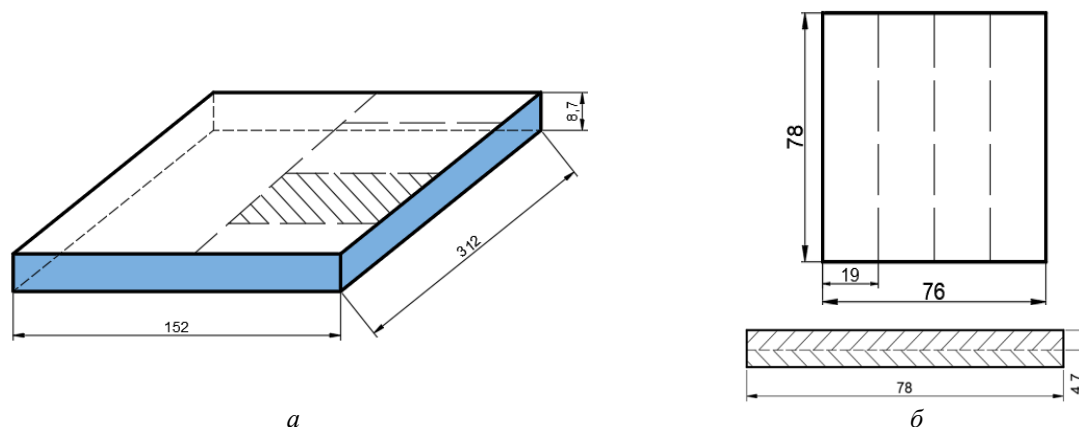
Схема вырезки образца из сваренного КМ (а) и подготовка образцов для прокатки (б)
